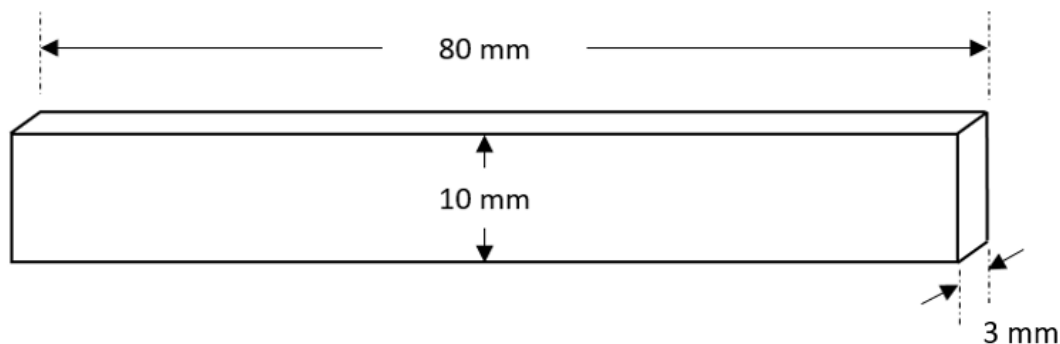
Dimensiones de las probetas de tracción para el PP-Silla
